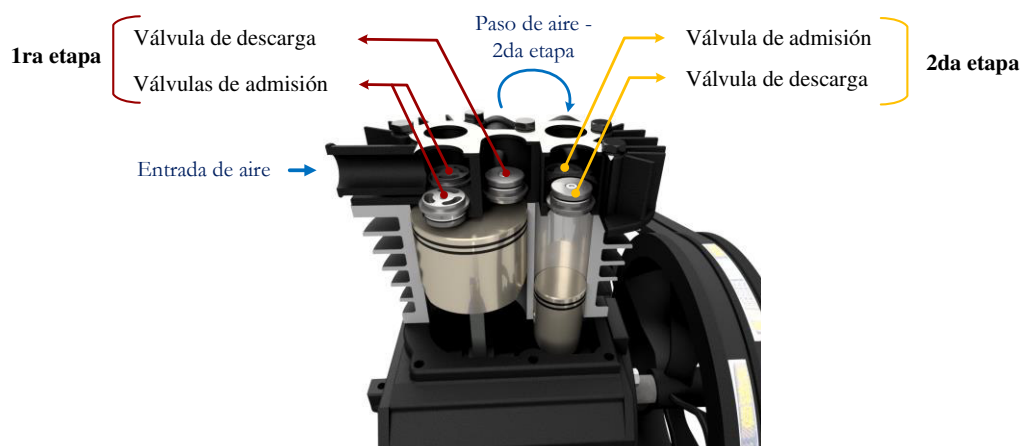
Vista en corte del compresor. Fuente: Propia.
